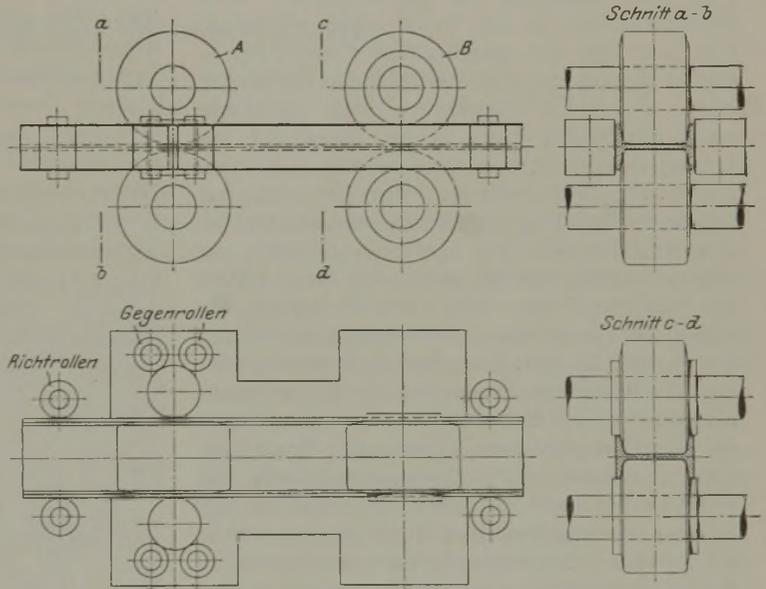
Walzwerk mit zwei Ständerpaaren. A u. B.
